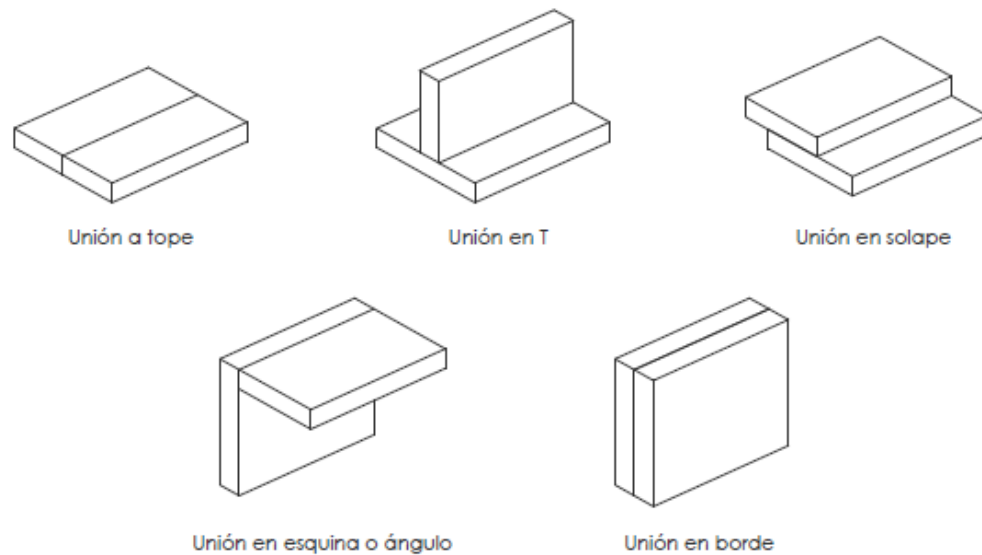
Tipo de uniones en el proceso de soldadura [19].
